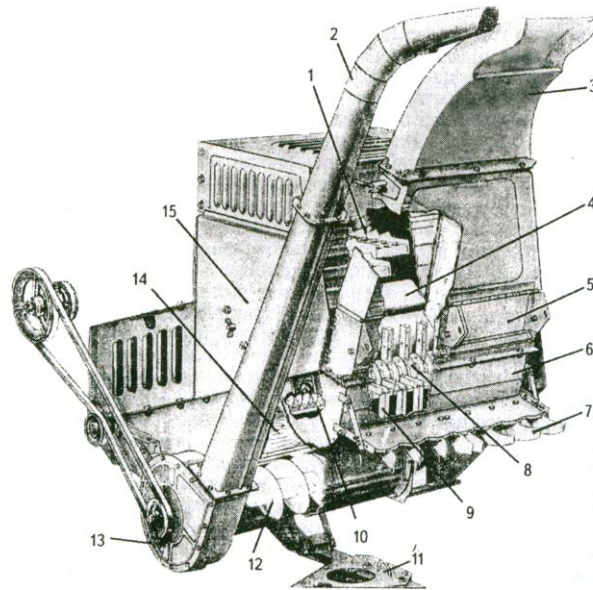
Вид копнителя зерноуборочного комбайна.
